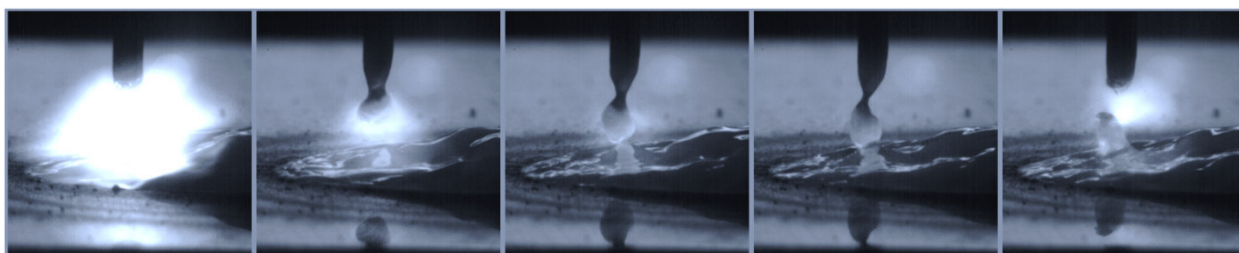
Процесс "перетекания" капли в сварочную ванну
